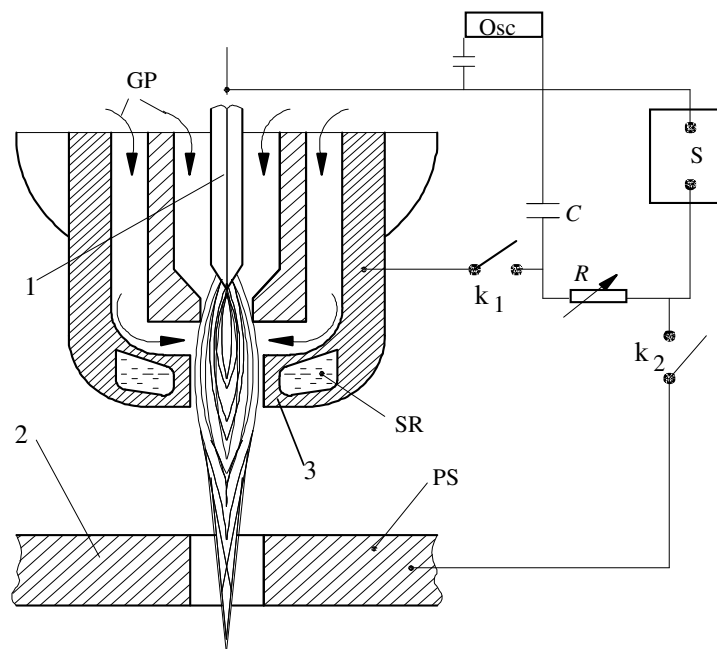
Schema de principiu a unei instalații de prelucrare dimensională cu plasmă:
